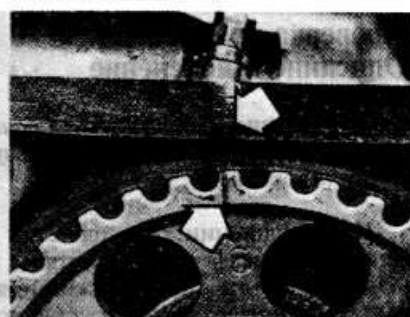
Установочная метка на звездочке распредвала совпадает с риской на задней крышке ремня — двигатель 1,6 л с впрыском топлива
